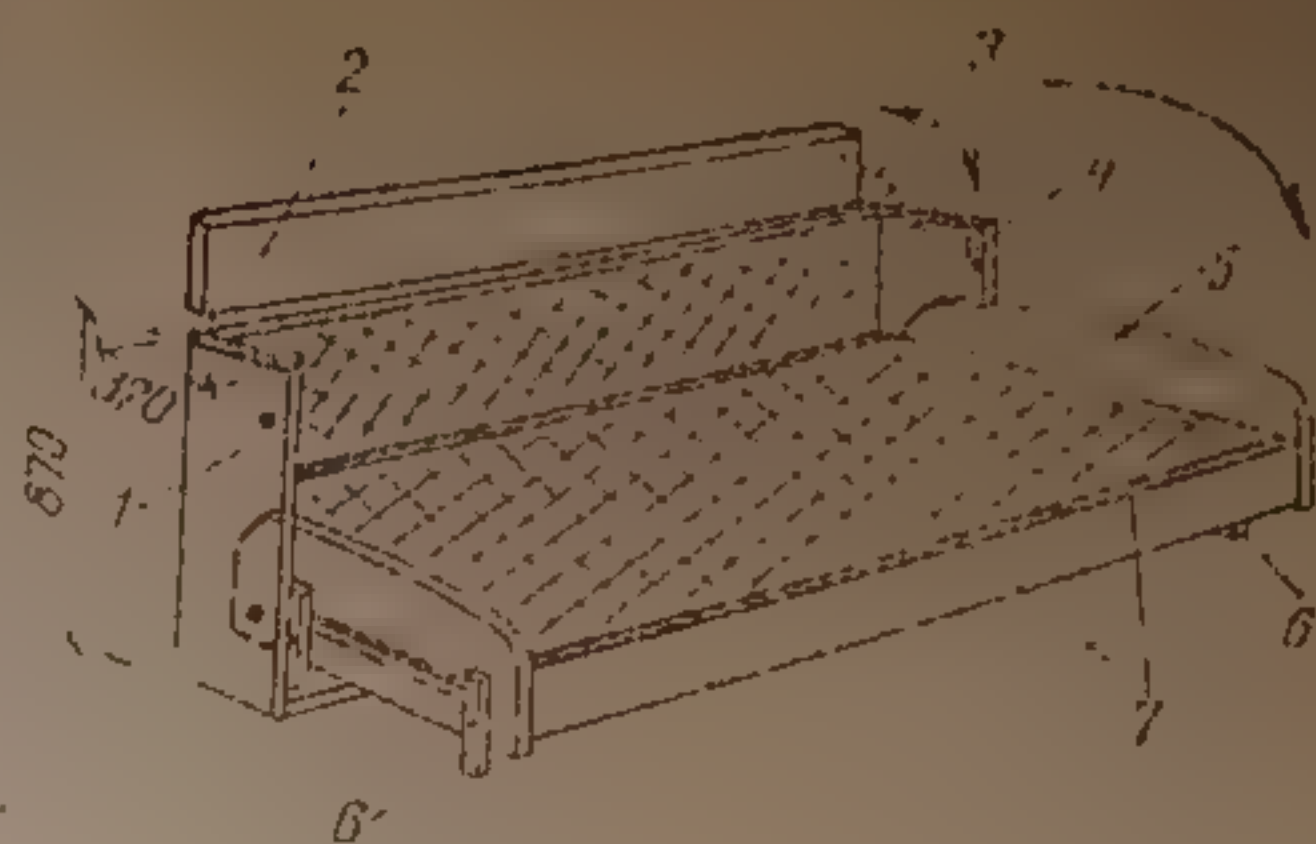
Трансформирующийся из двухъярусной кровати с положением «кровать»: 1 — боковина; 2 — откидная доска; 3 — держатель-фиксатор; 4 — защелка-фиксатор; 5 — боковины (крылья) кровати-стола; 6 — опорные ножки; 7 — прижимные ленты
